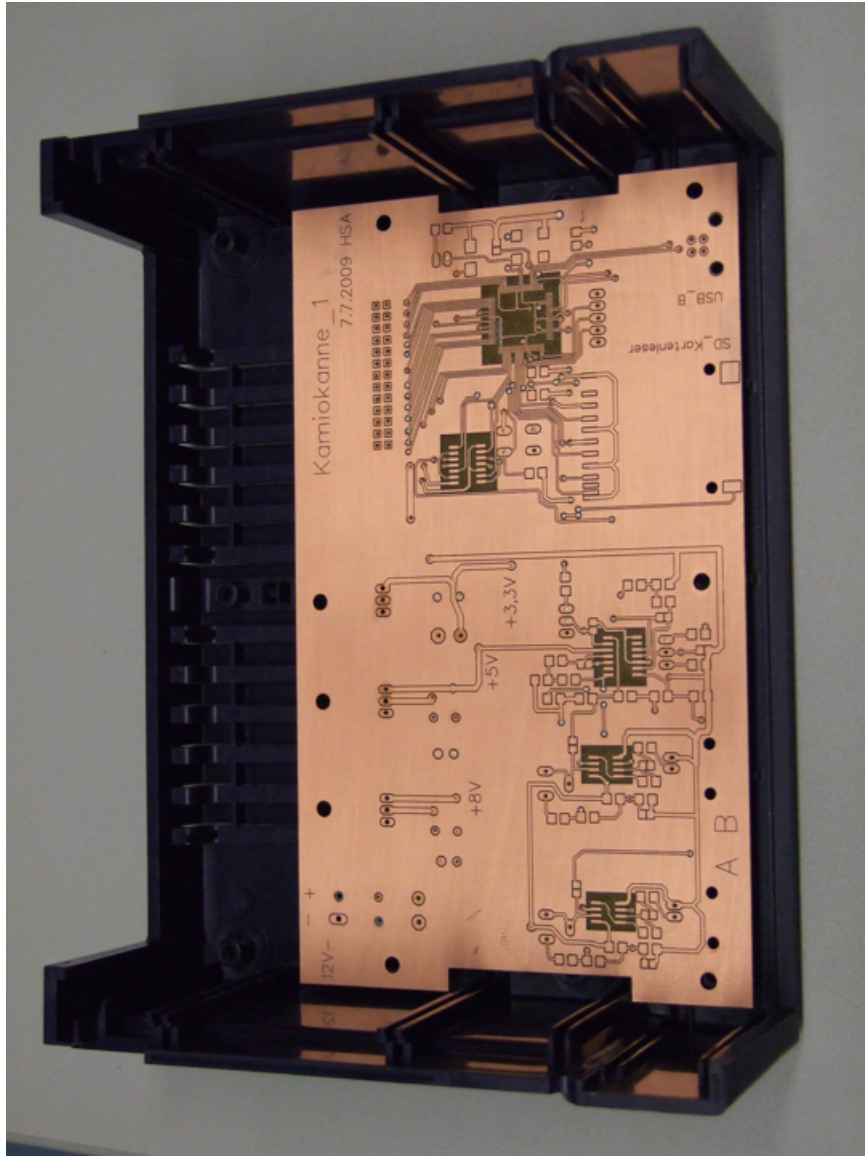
unbestückter gefräster Prototyp der Hauptplatine in einem Gehäuse der Firma PHYWE.
